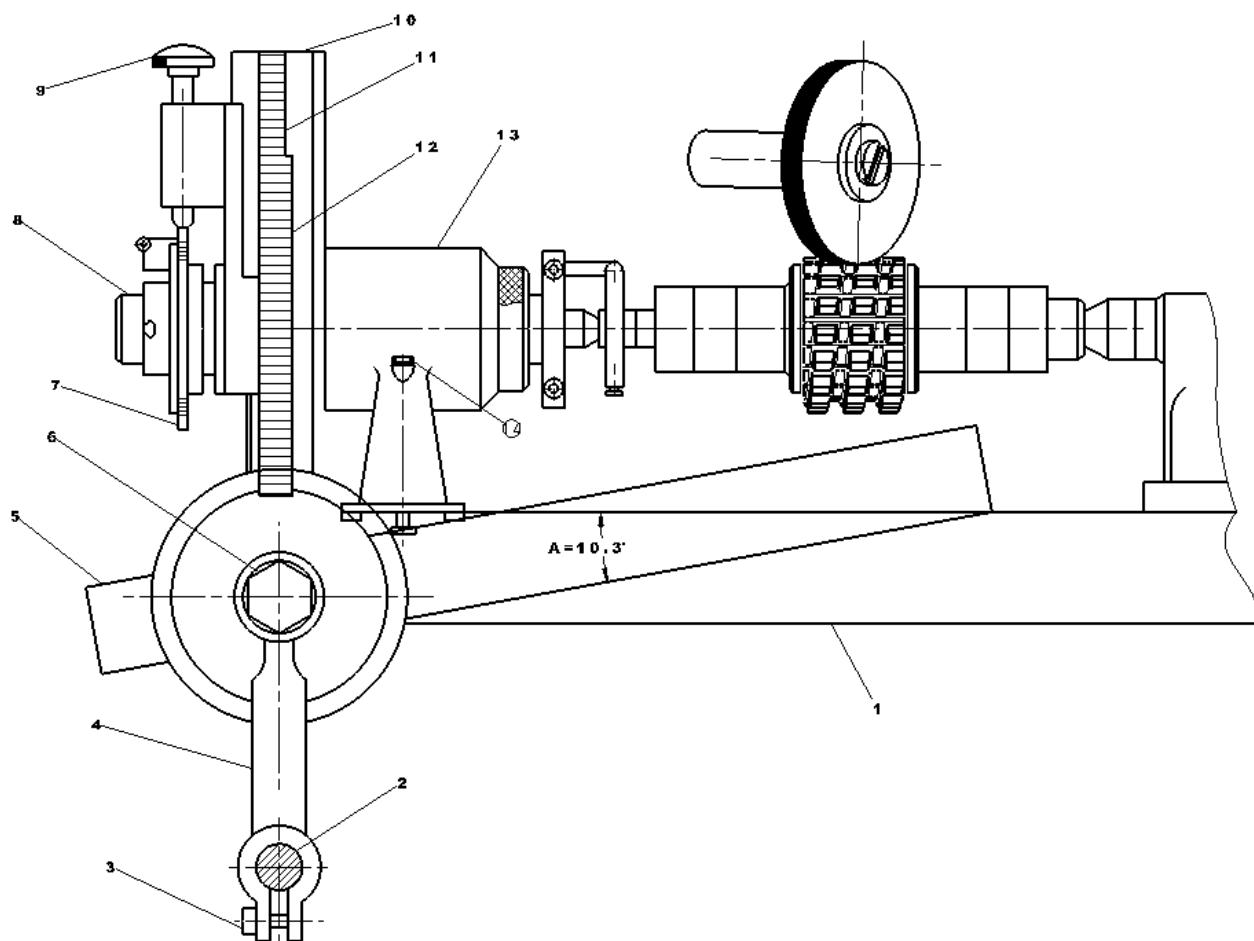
Схема пристосування для переточування черв'ячних фрез на універсально-заточувальному верстаті
